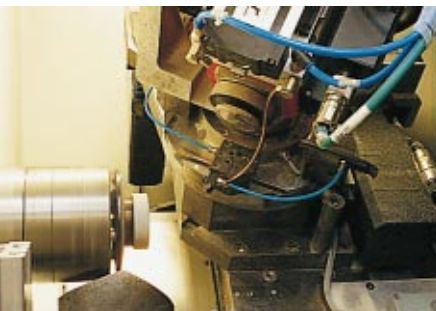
Arbeitsraum der Werkzeugmaschine mit schwenkbarem Lasereinheit und Werkzeugdrehtisch.
